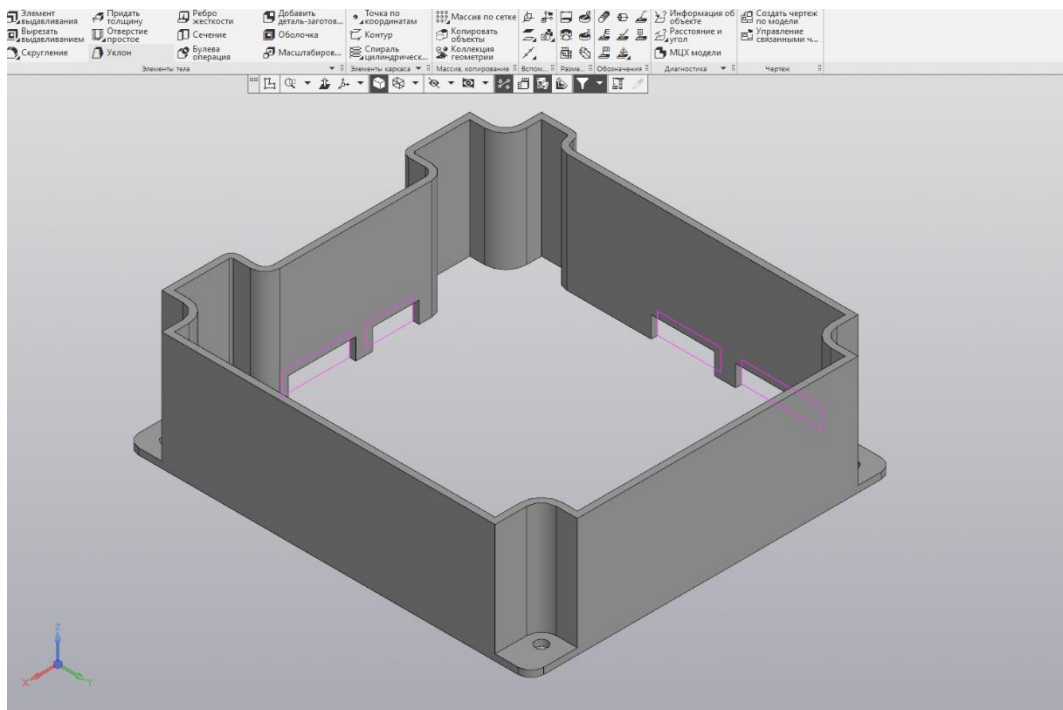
Создание отверстий под кабели первого корпуса
